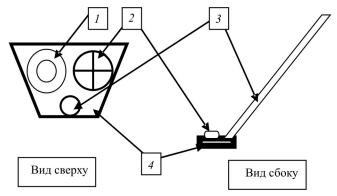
Конструктивная схема приспособления для проведения замеров освещенности на объектах повышенной опасности: 1 – жидкостный уровень; 2 – фотоэлемент люксметра; 3 – крепление ручки, ручка; 4 – корпус приспособления
